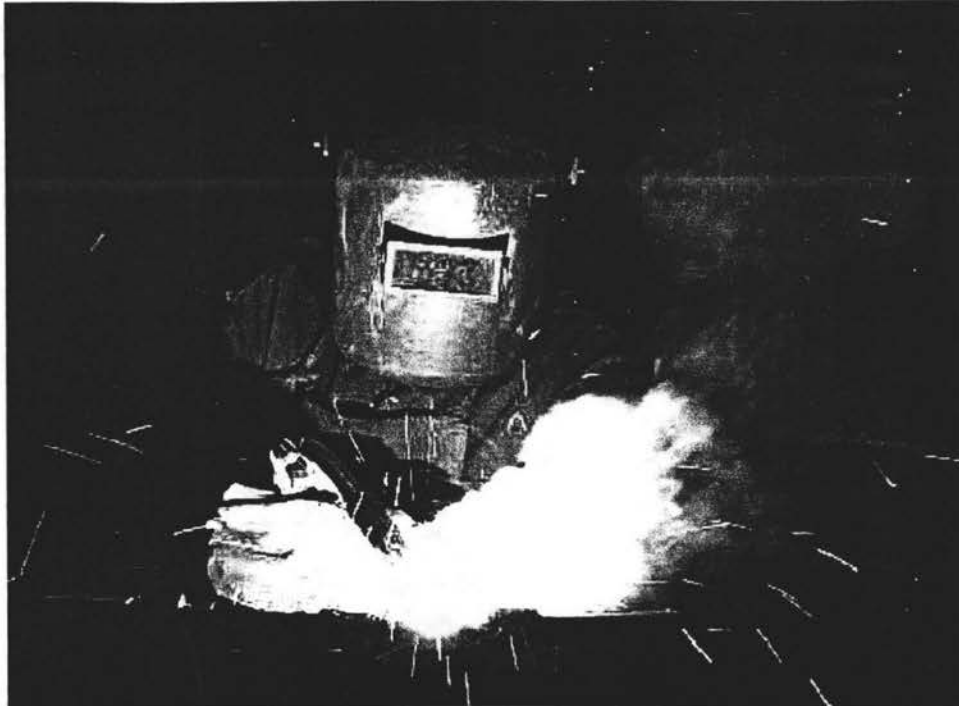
Muestra a un soldador aplicando una soldadura de penetración.
